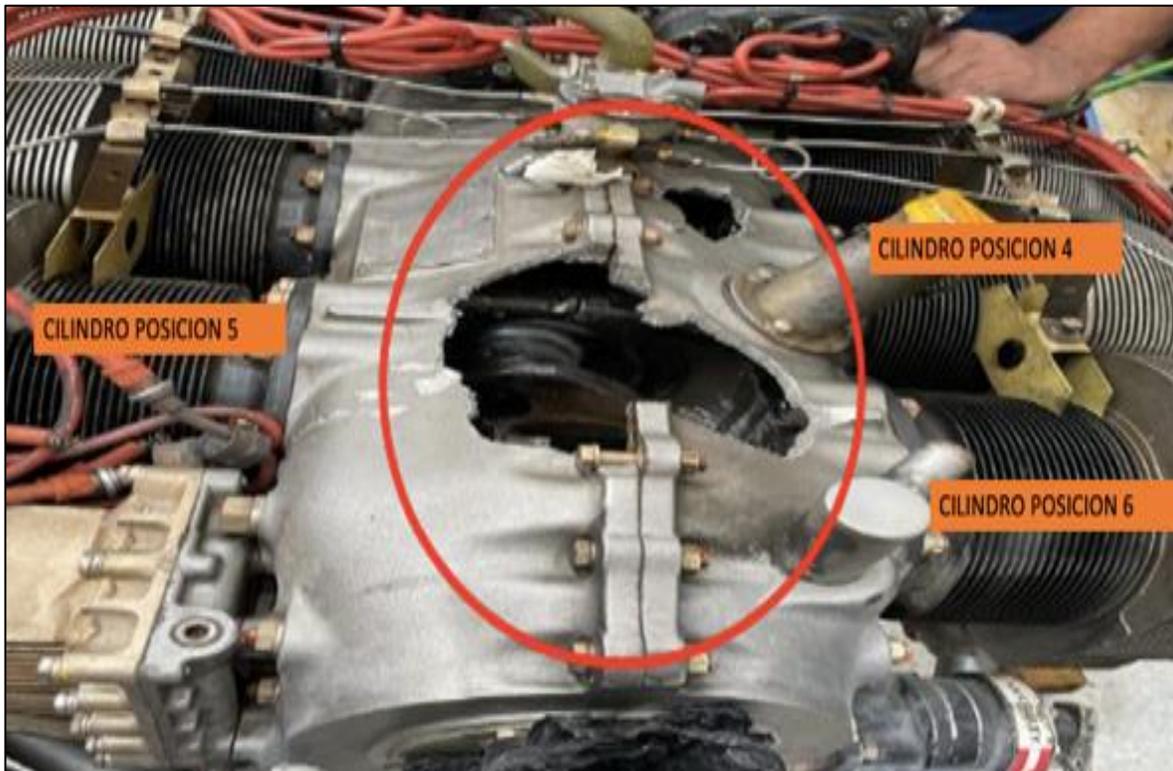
Inspección motor Continental instalado en el HK-2014.
